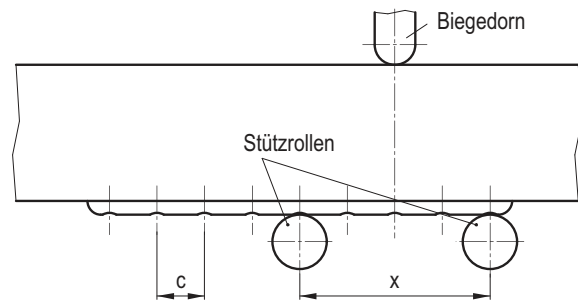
Abmessung des Prüfstücks für den Biegeversuch von Hartauftragsschweißungen
